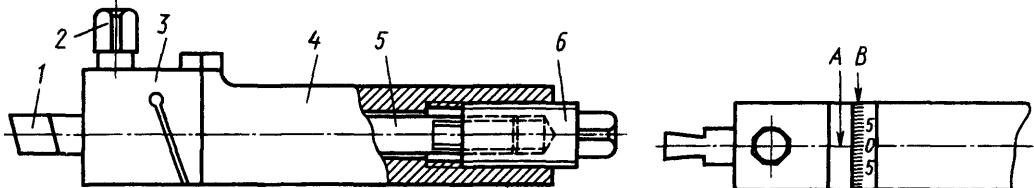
Державка с поворотной головкой для резьбового резца
